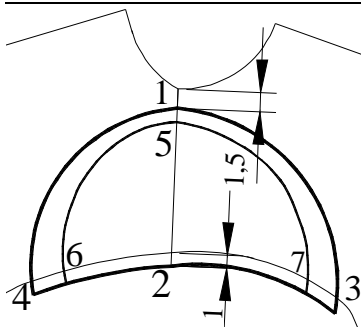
Креслення деталей плечової накладки для двобічного жакета
